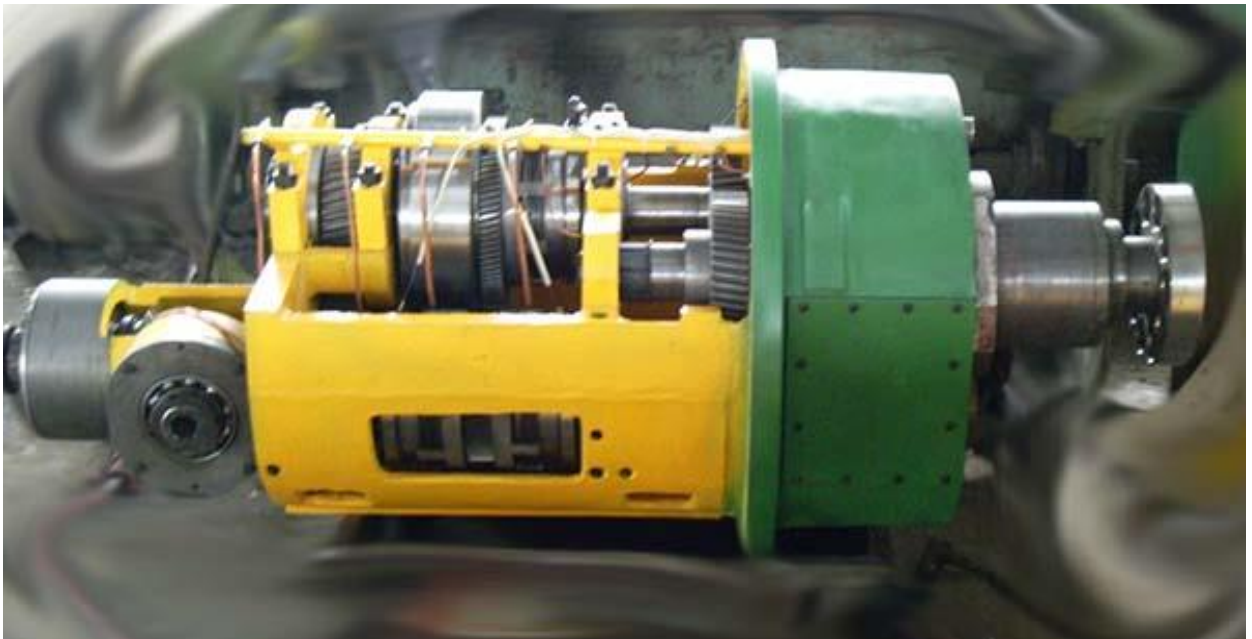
Коробка швидкостей токарно-карусельного верстата 1516
